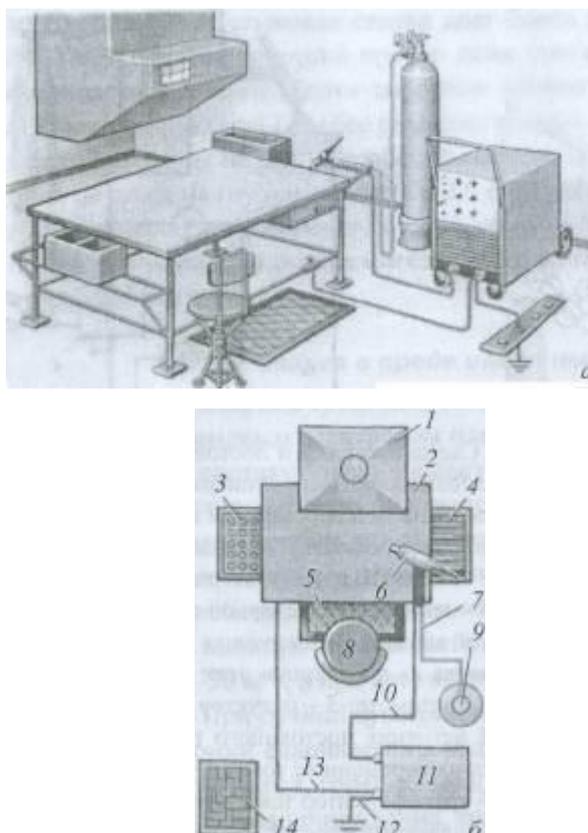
Схема поста аргонодуговой сварки
